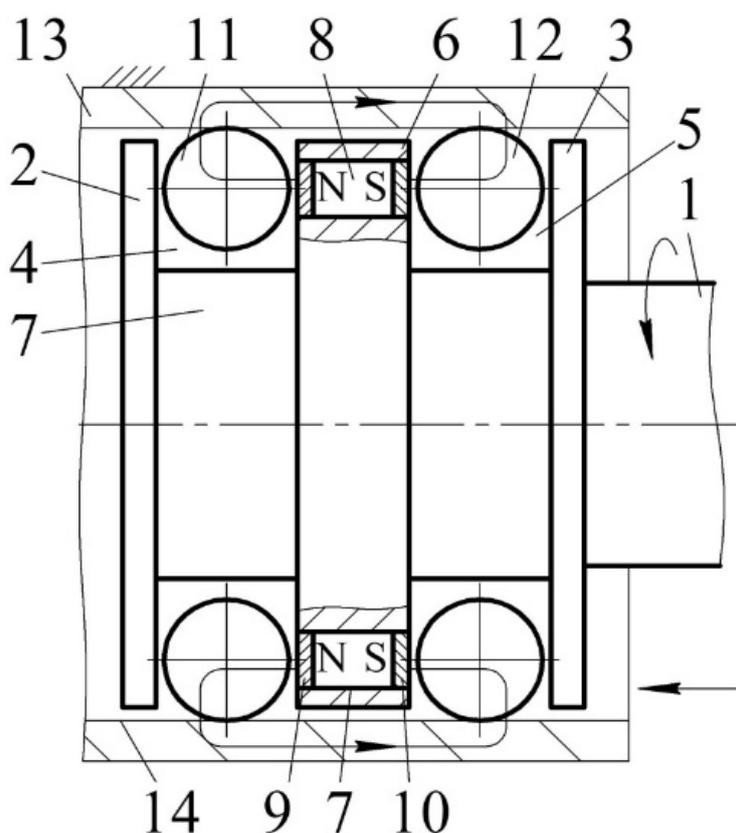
Двухрядный инструмент для КМДО цилиндрической поверхности отверстия
